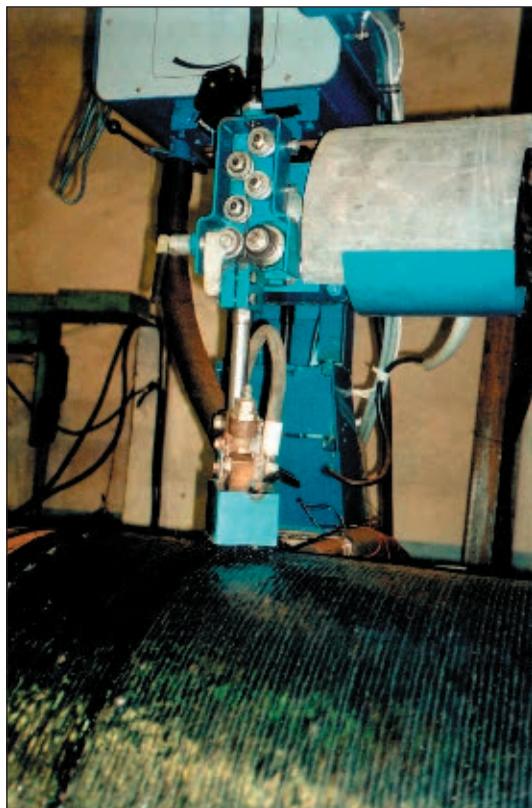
Наплавка подслоя на вал поворотно-лопастной гидротурбины мощностью 250 МВт: внешний вид наплавленной поверхности
